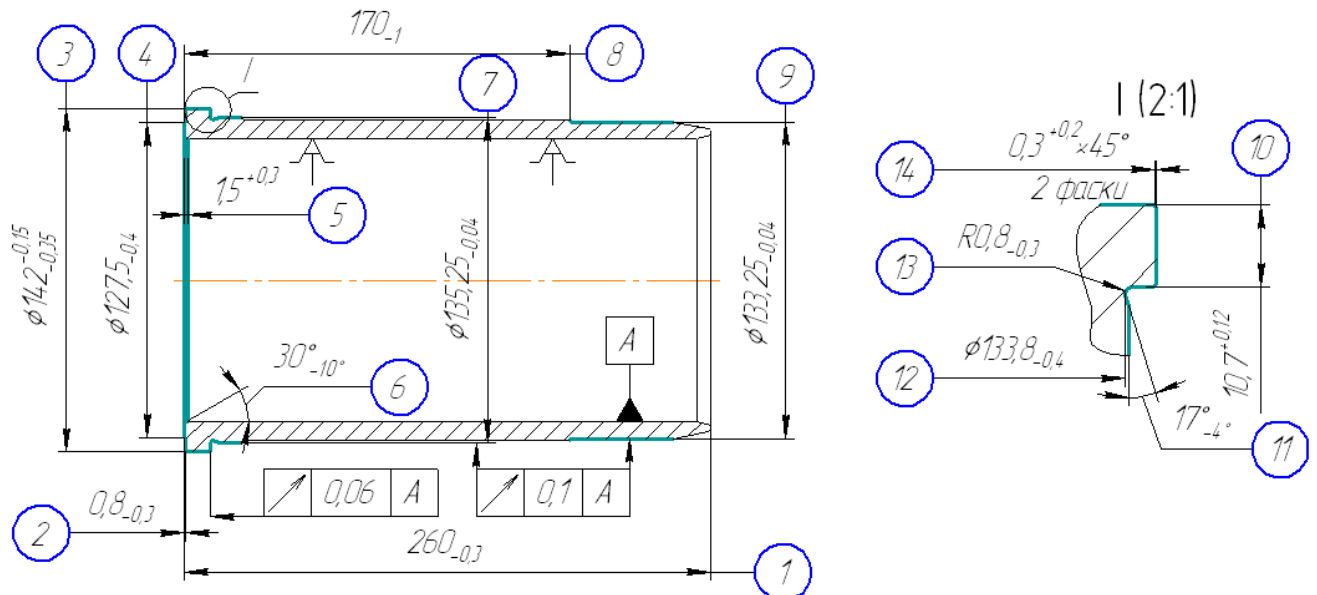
Ескіз токарної багаторізевої операції
